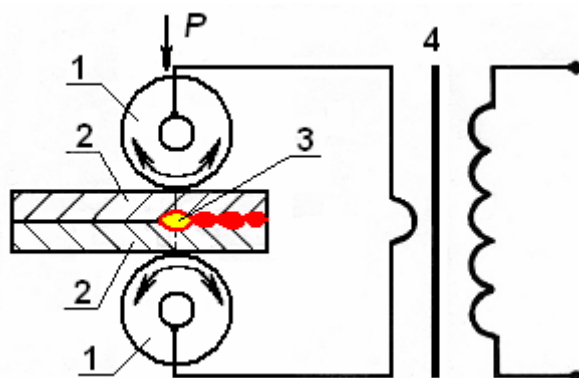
Схема шовной электроконтактной сварки
